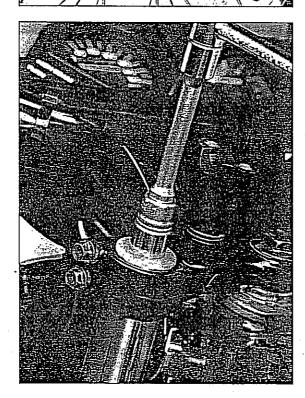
Gabelklemmfaust lockem und Verschluss-Schraube ausdrehen
